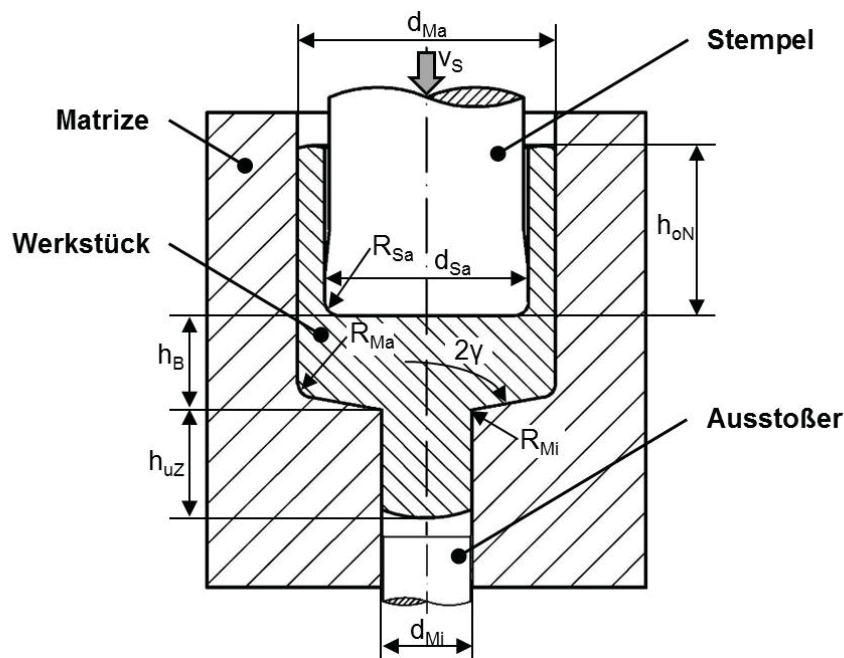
Prinzipskizze des VV-NR-FP mit einem bewegten Werkzeugelement (Stempel)
